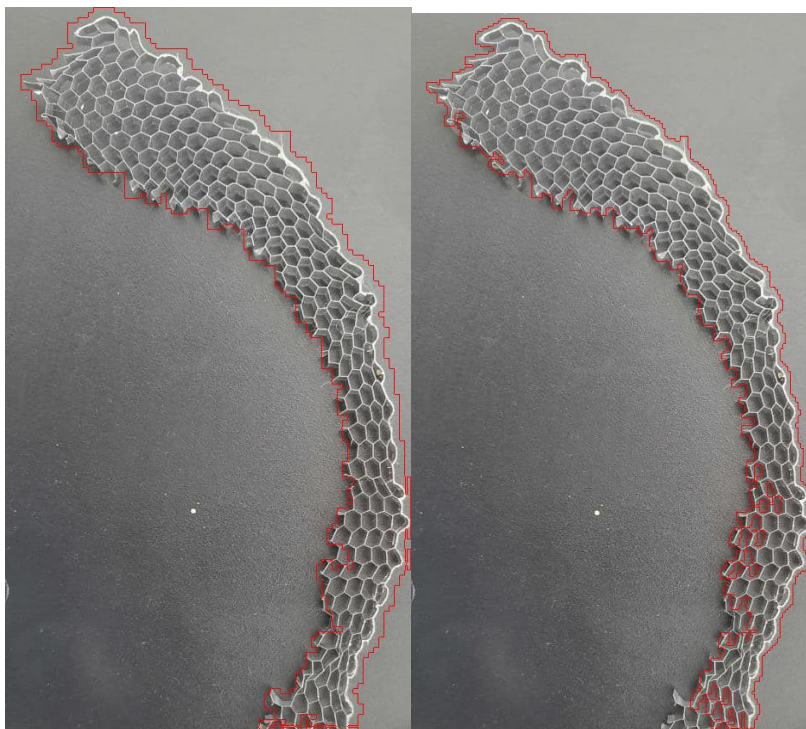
Контур заготовки, полученный матрицей с малым ядром.
